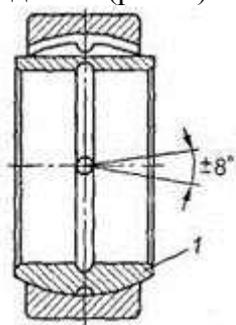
Самоустанавливающийся подшипник: 1 — вкладыш
